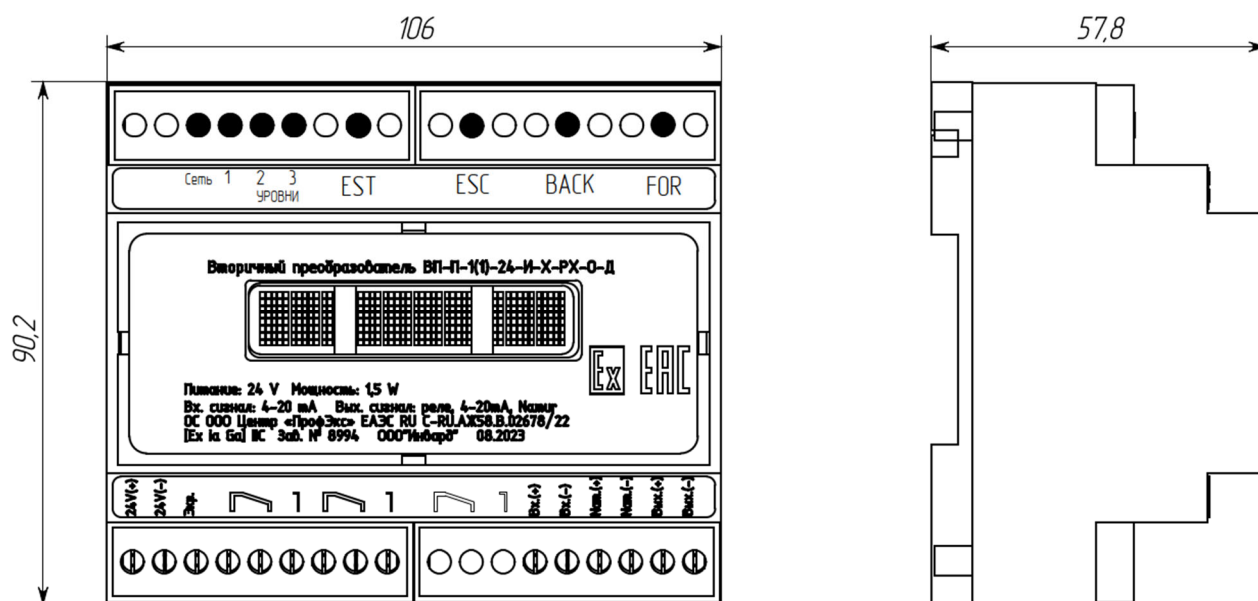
Габаритные и установочные размеры вторичного преобразователя до четырёх датчиков со степенью защиты корпуса IP40 и креплением на DIN-рейку.
